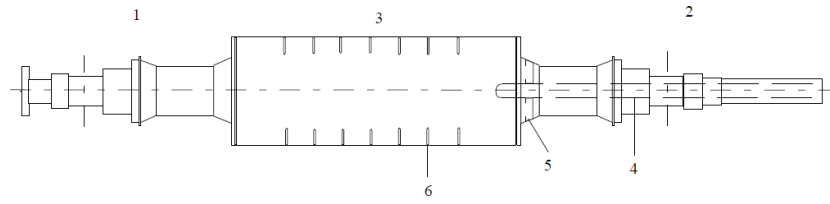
Corps du rotor de l'alternateur WY21Z-092RR. [2]
